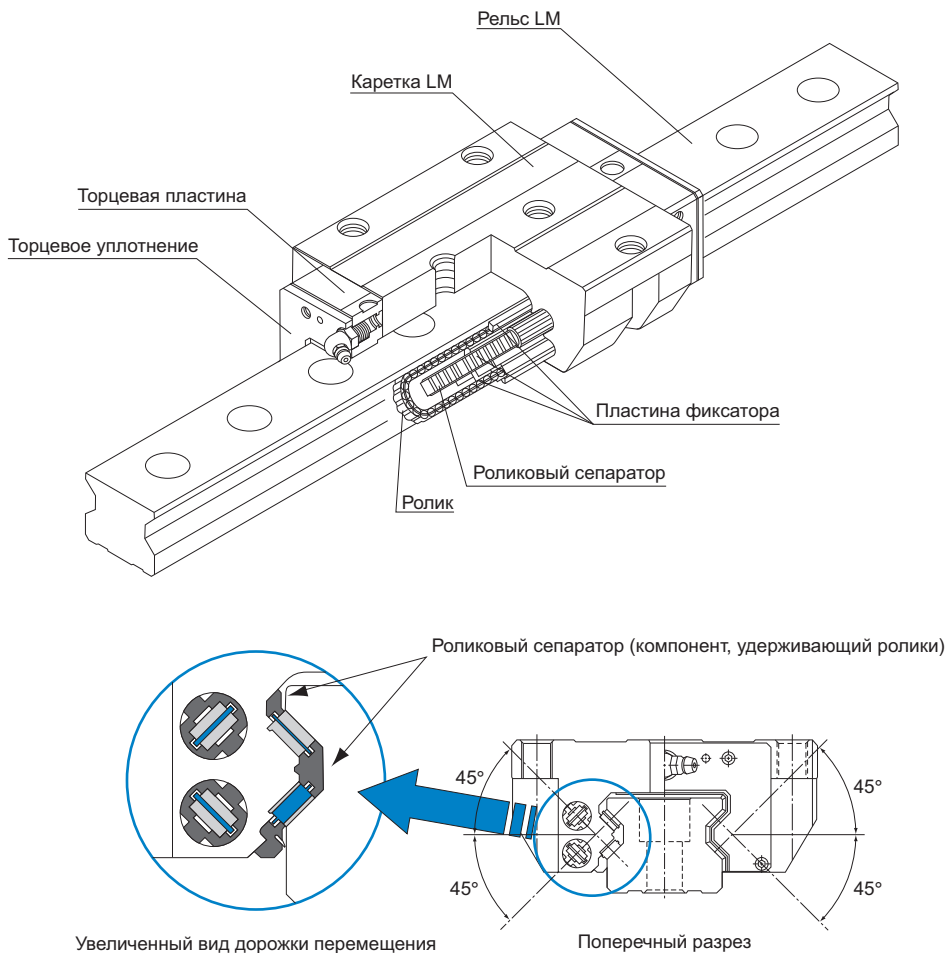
Чертеж конструкции роликовой рельсовой направляющей LM с сепаратором модели SRG
